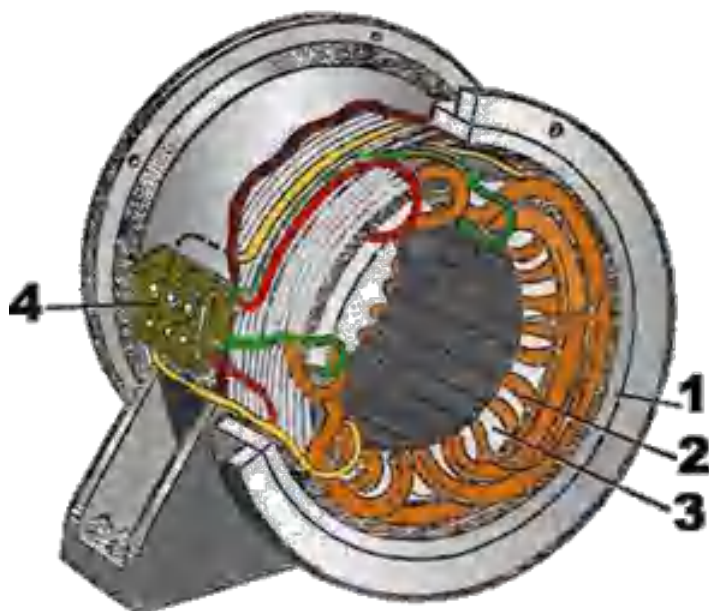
Будова статора асинхронного двигуна: 1 – осердя; 2 – обмотка; 3 – станина; 4 – щиток.
